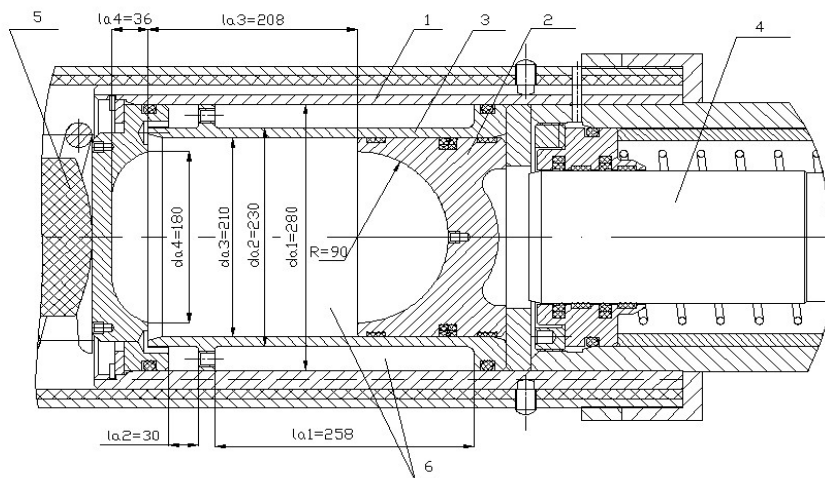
Параметризована конструктивна схема камери пневмоакумулятора гідромолота: 1 – корпус; 2-поршень пневмоакумулятора; 3- циліндр поршня; 4- бойок ; 5- амортизаційний елемент; 6- пневмокамера.
